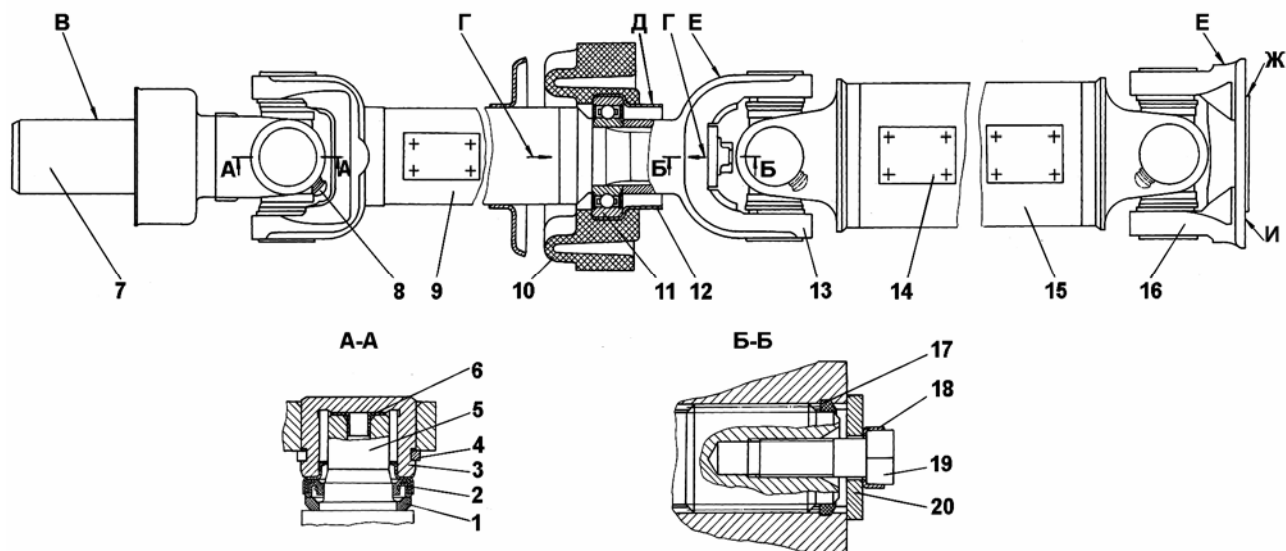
Карданная передача с промежуточной опорой: Е – места допустимых ударов при разборке; 1 – отражатель; 2 – манжета; 3 – игольчатый подшипник; 4 – стопорное кольцо; 5 – крестовина; 6 – торцовая шайба; 7 – скользящая вилка; 8 – пресс-масленка с колпачком; 9 – промежуточный карданный вал; 10 – подушка опоры; 11 – подшипник промежуточной опоры; 12 – обойма; 13 – шлицевая вилка; 14 – балансировочная пластина; 15 – задний карданный вал; 16 – фланец; 17 – кольцо уплотнительное; 18 – стопорная пластина; 19 – болт; 20 – шайба
